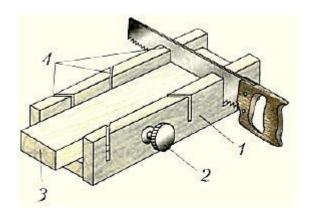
Пиление в стусле: 1 — стусло; 2 — прижимной винт; 3 — заготовка; 4 — пропилы
